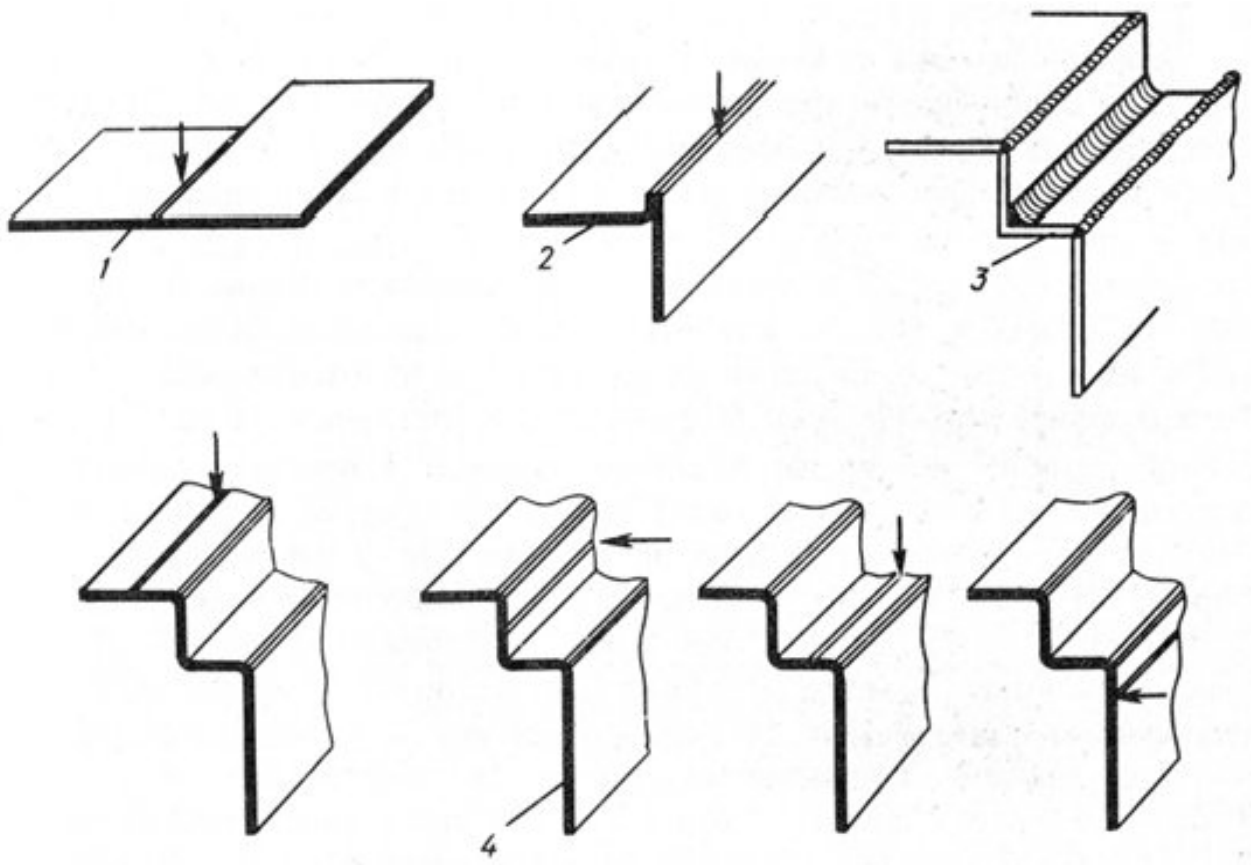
Подготовка кромок тонких листов под сварку:
